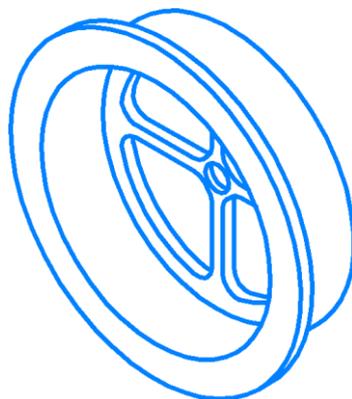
Внешний вид приспособления для входного и выходного окон.
